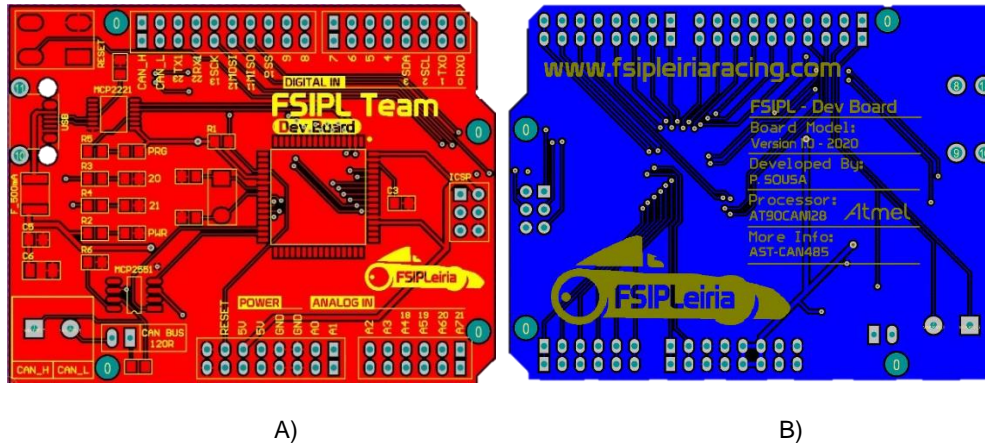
Design Final da "Devboard 1.0" - 2D. A) Top Layer, B) Bottom Layer.
